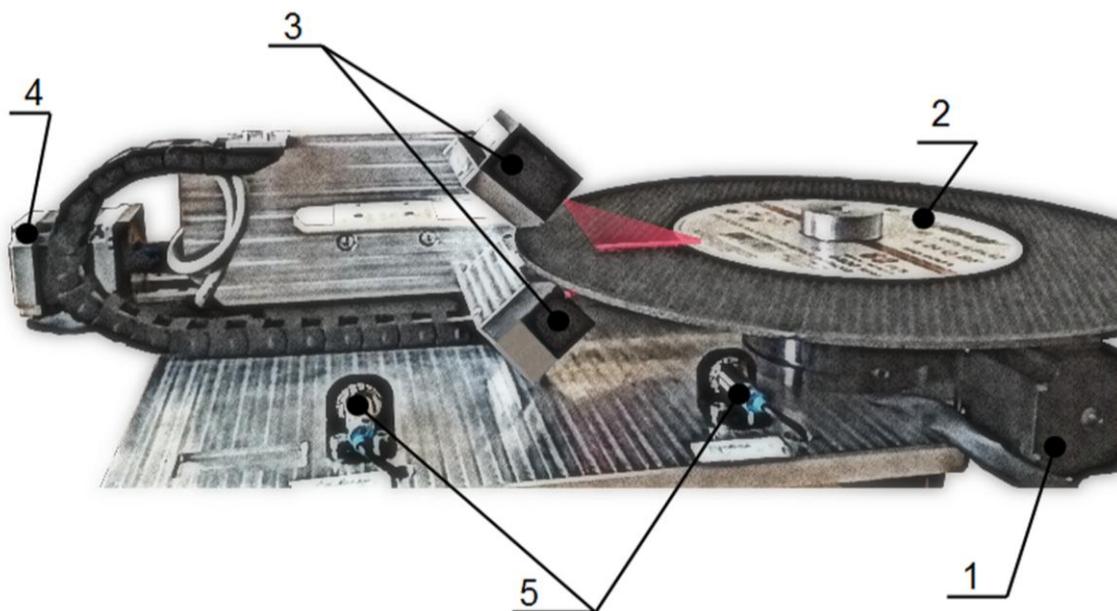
Устройство установки: 1 – шаговый двигатель поворота; 2 – контролируемый диск; 3 – лазерные сканеры LS2D; 4 – шаговый двигатель перемещения; 5 – концевые датчики.
